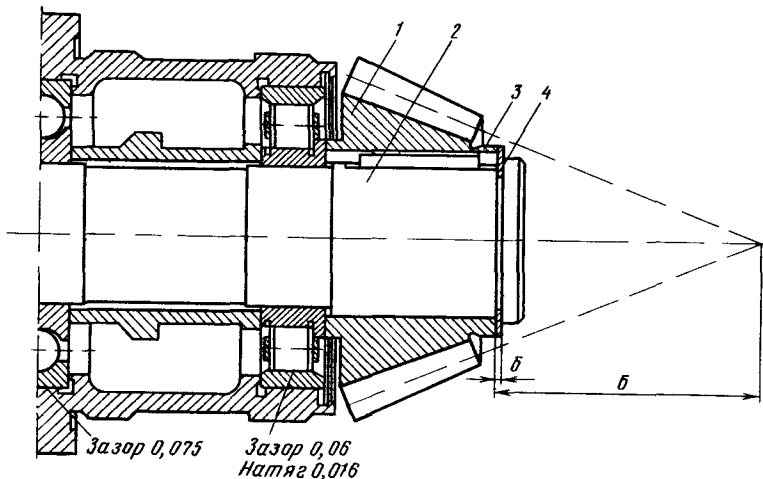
Установка кольца, регулирующего зазор между зубьями конических зубчатых колес вертикальной передачи:
